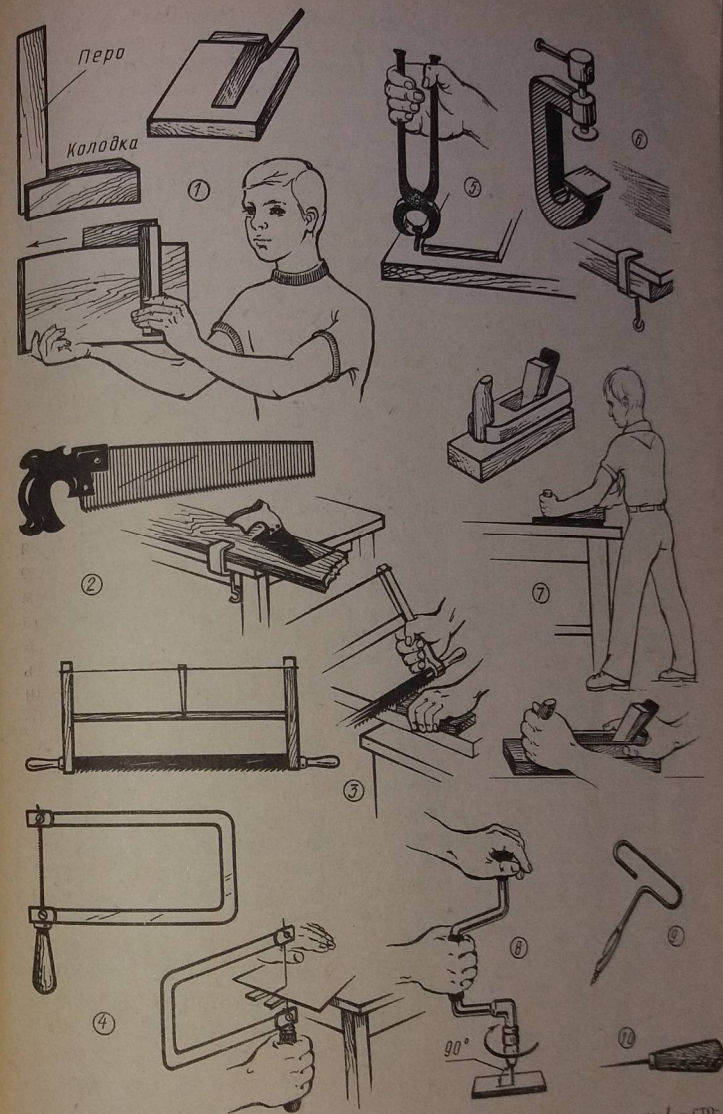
Столярный инструмент, приспособления и приемы работы ими: 1—столярный угольник; 2—столярная ножовка; 3—лучковая пила; 4—лобзик; 5—столярные клещи; 6—струбцина; 7—рубанок; 8—коловорот; 9—буравчик; 10—шило
